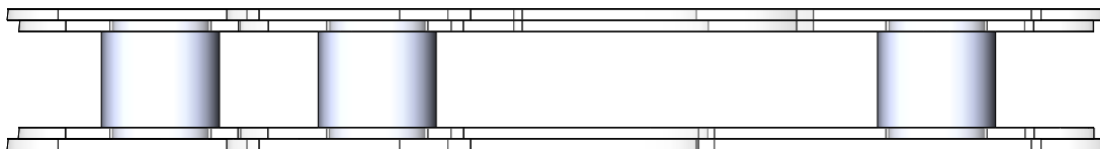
Сборка 3D модели модуля из ПВХ. Вид слева.
